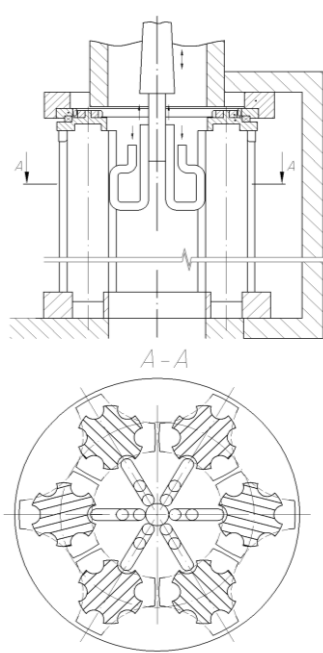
Пристрій-супутник для групового гартування поверхонь шліцевих валів
